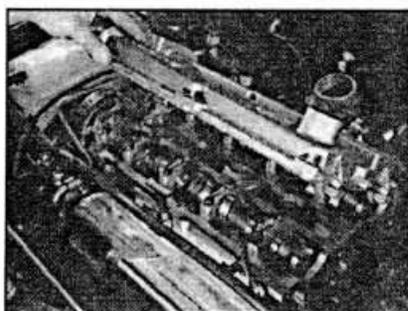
С.4. Снятие крышки головки блока цилиндров.
